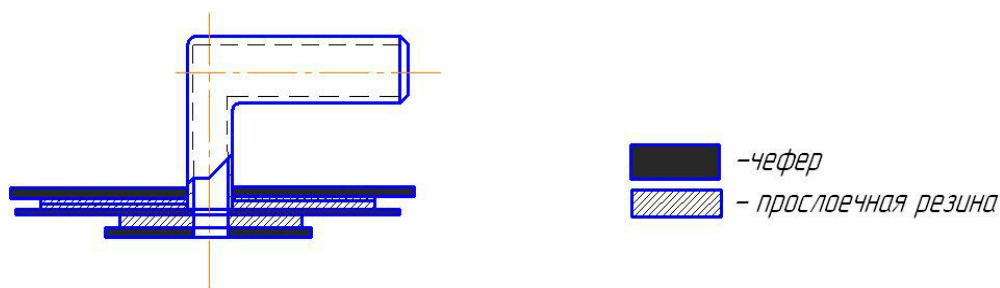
Изготовление вентиля пневмобаллона
